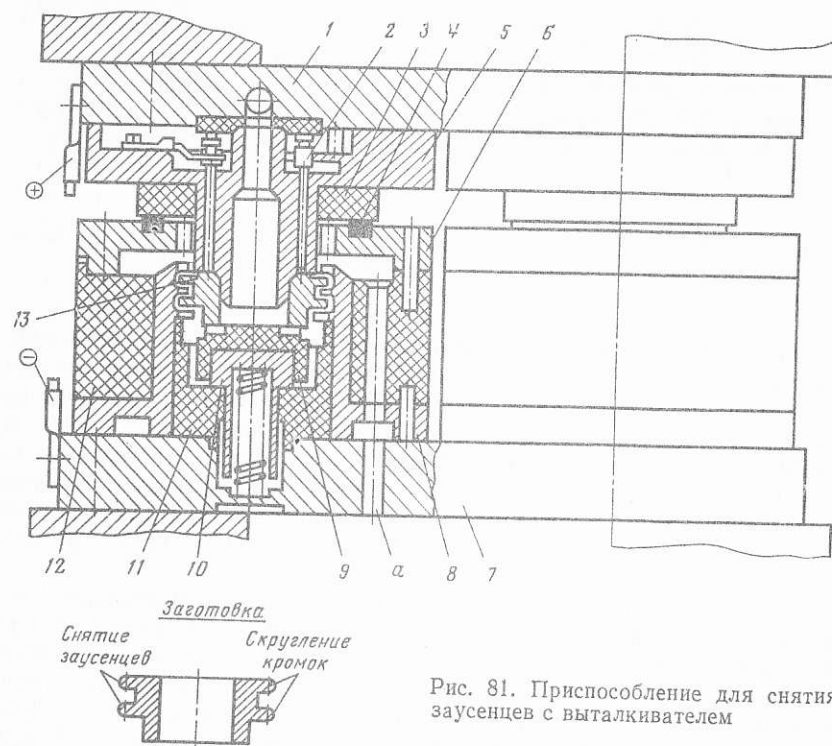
Приспособление для снятия заусенцев с выталкивателем
